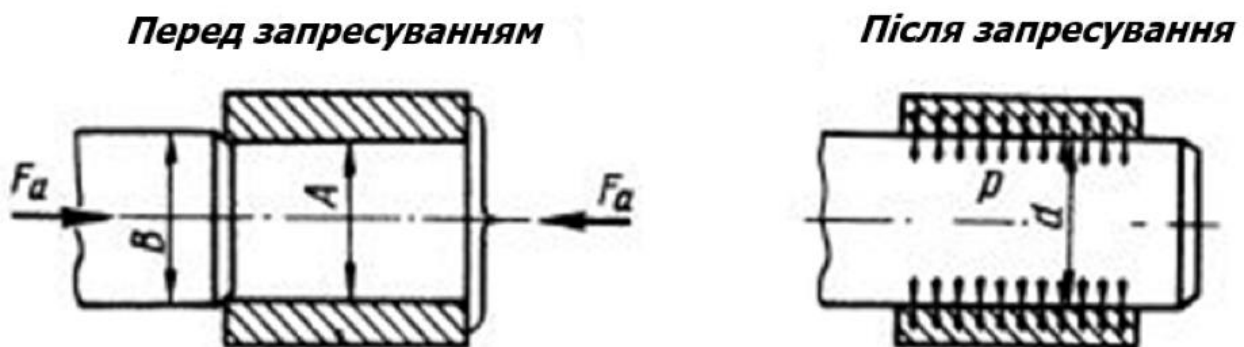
Схема зміни розмірів деталей під час запресування
